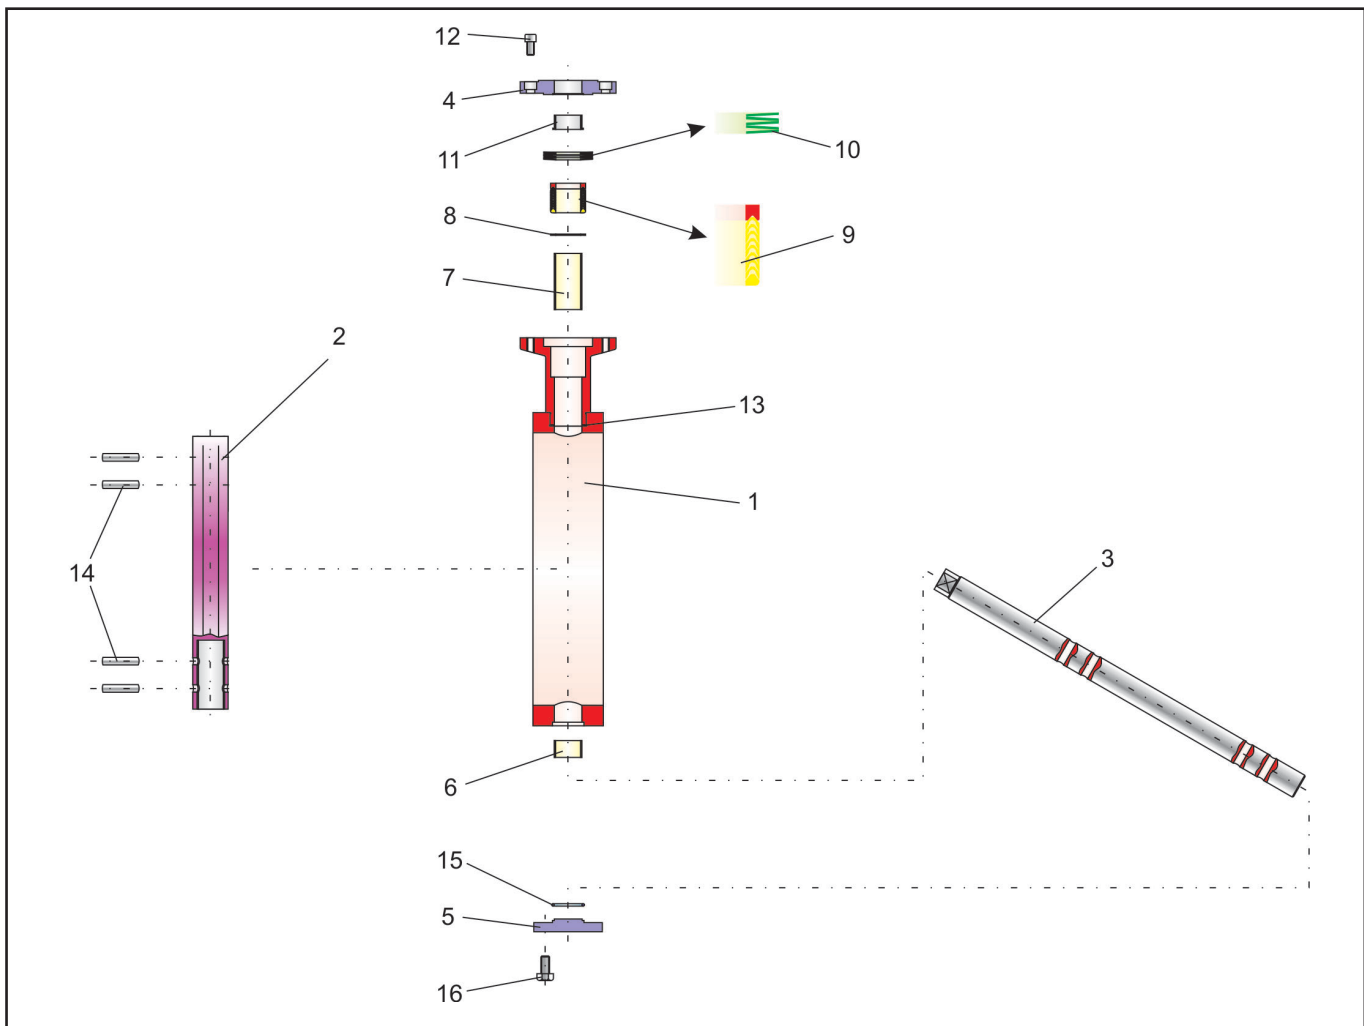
Explosionszeichnung der Regelklappe BR 14e
